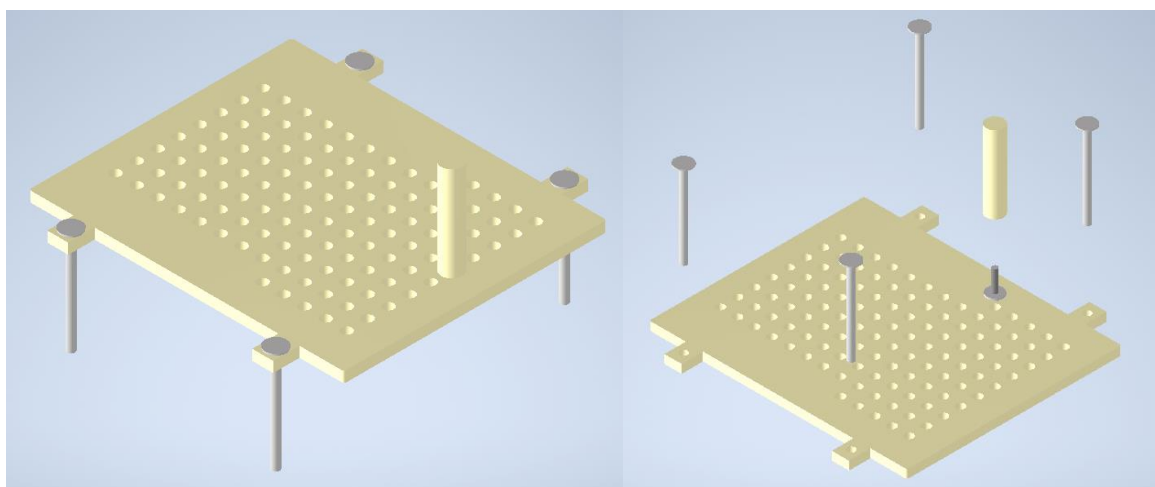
Montagem e desmontagem do PegBoard RJ23-01 (autoria própria).
